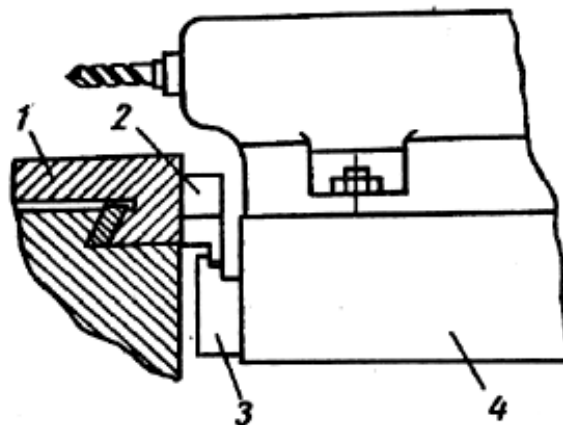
Установка свердла 1 – супорт; 2, 3 – планка; 4 – задня бабка
